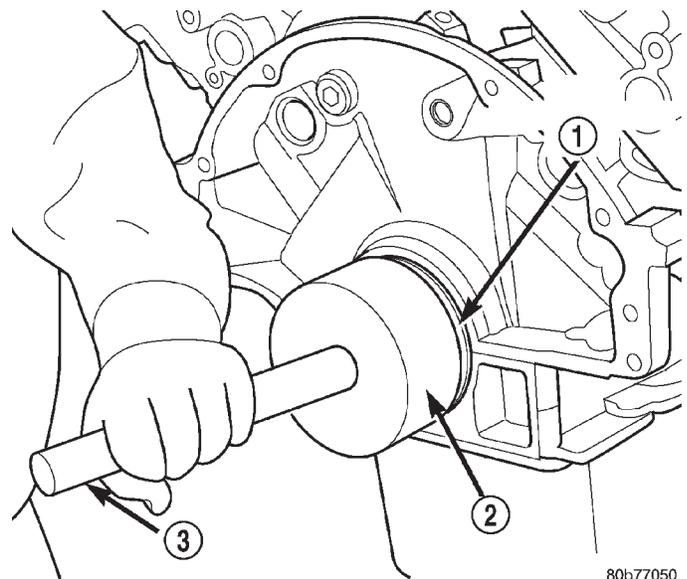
Einbau des hinteren Kurbelwellendichtrings
